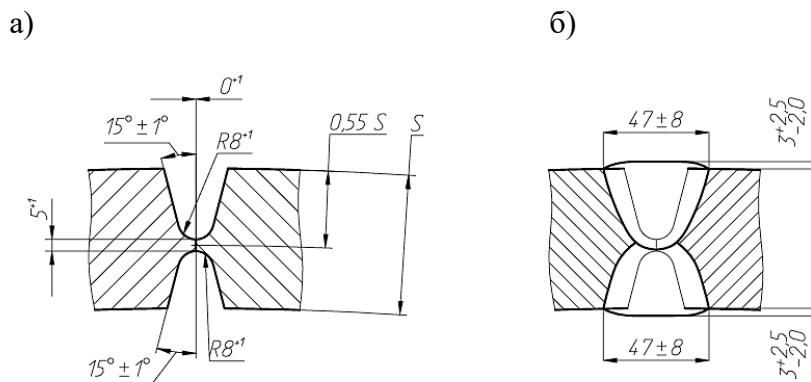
а) разделка кромок под сварку с углом $15^{\circ} \pm 1^{\circ}$, б) выполненное сварное соединение
